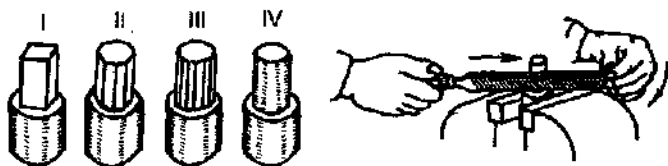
Опиливание цилиндрических заготовок: I — квадрат; II — восьмигранник; III — шестнадцатигранник; IV — цилиндр
